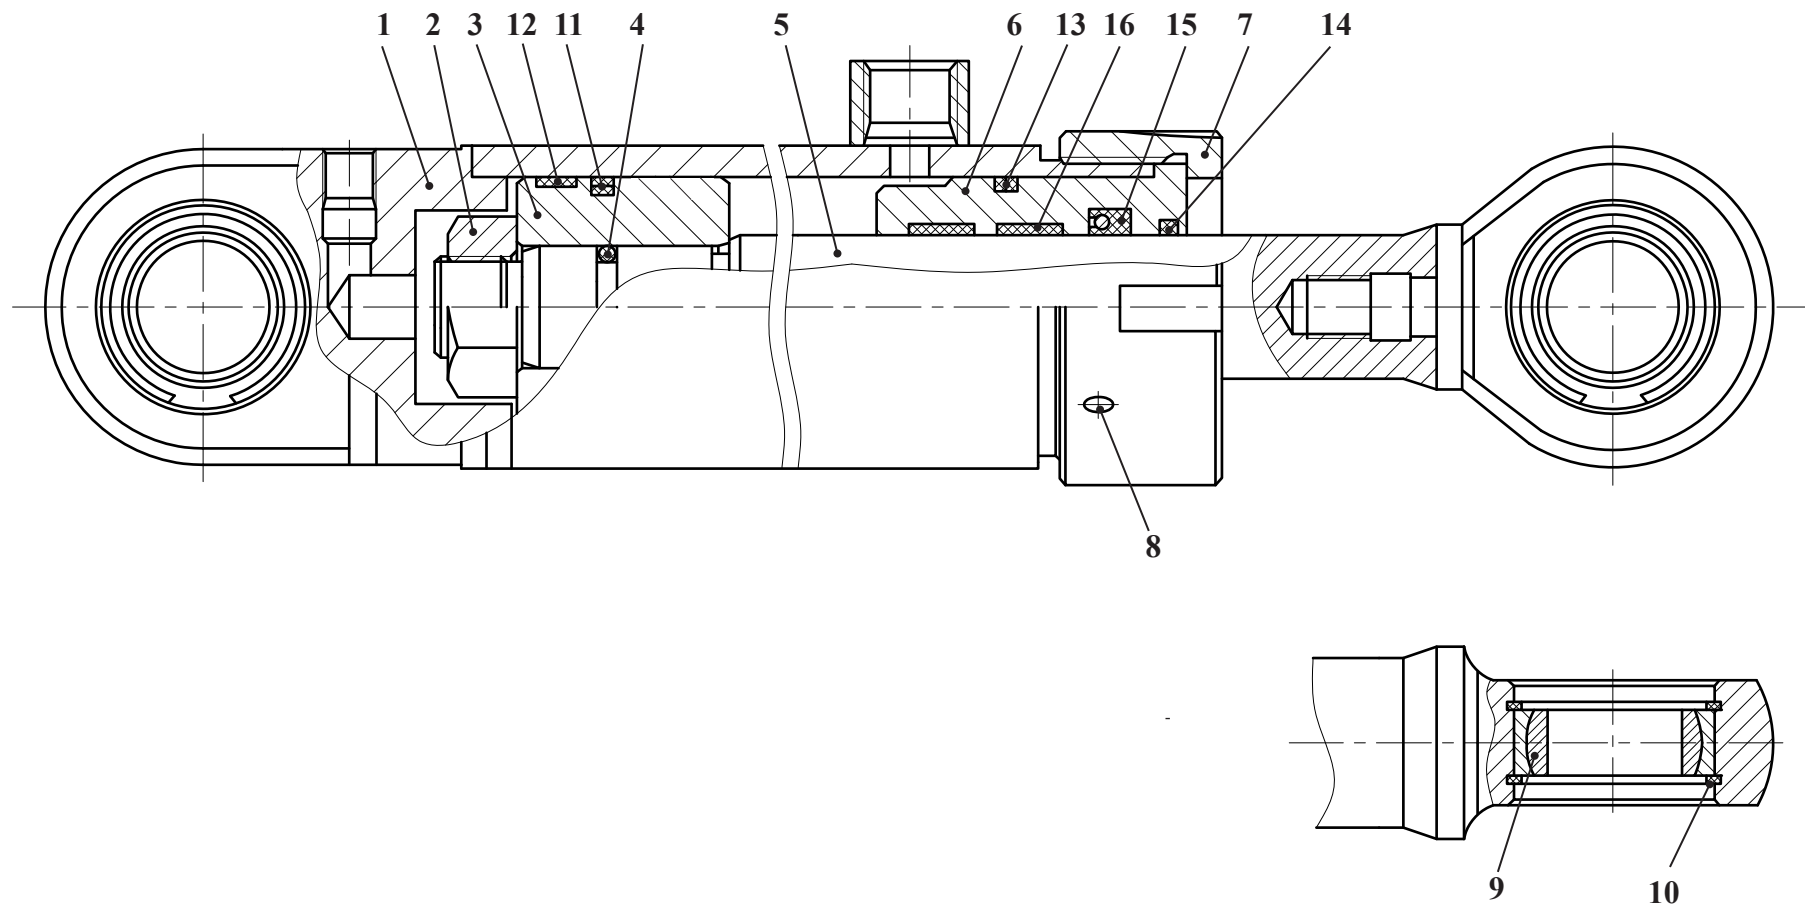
ЦГ-80.56x400.765.11.001	Гидроцилиндр
